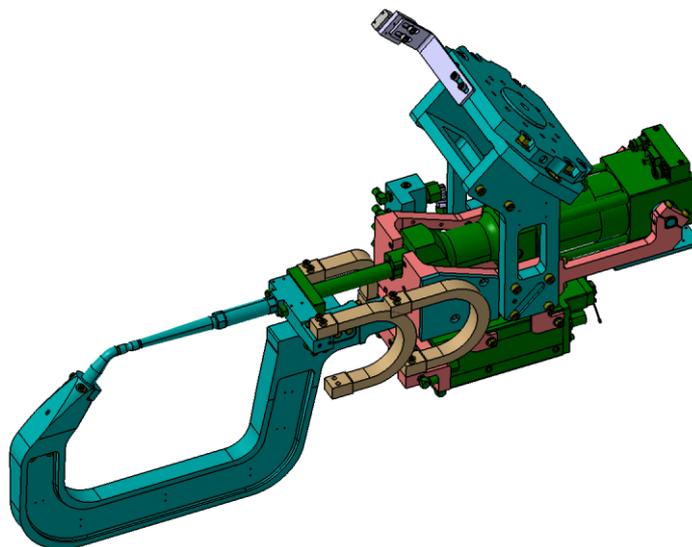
Сварочный пистолет F210866850025579_c_zange
